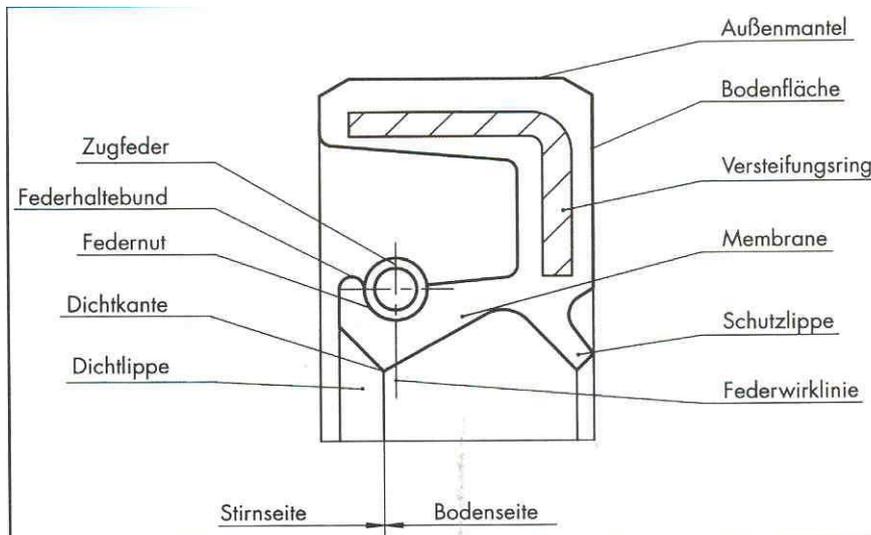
Kennzeichnungen am Radial-Wellendichtring (Auszug aus ISO 6194) Standard Bauformen Dichtlippe
